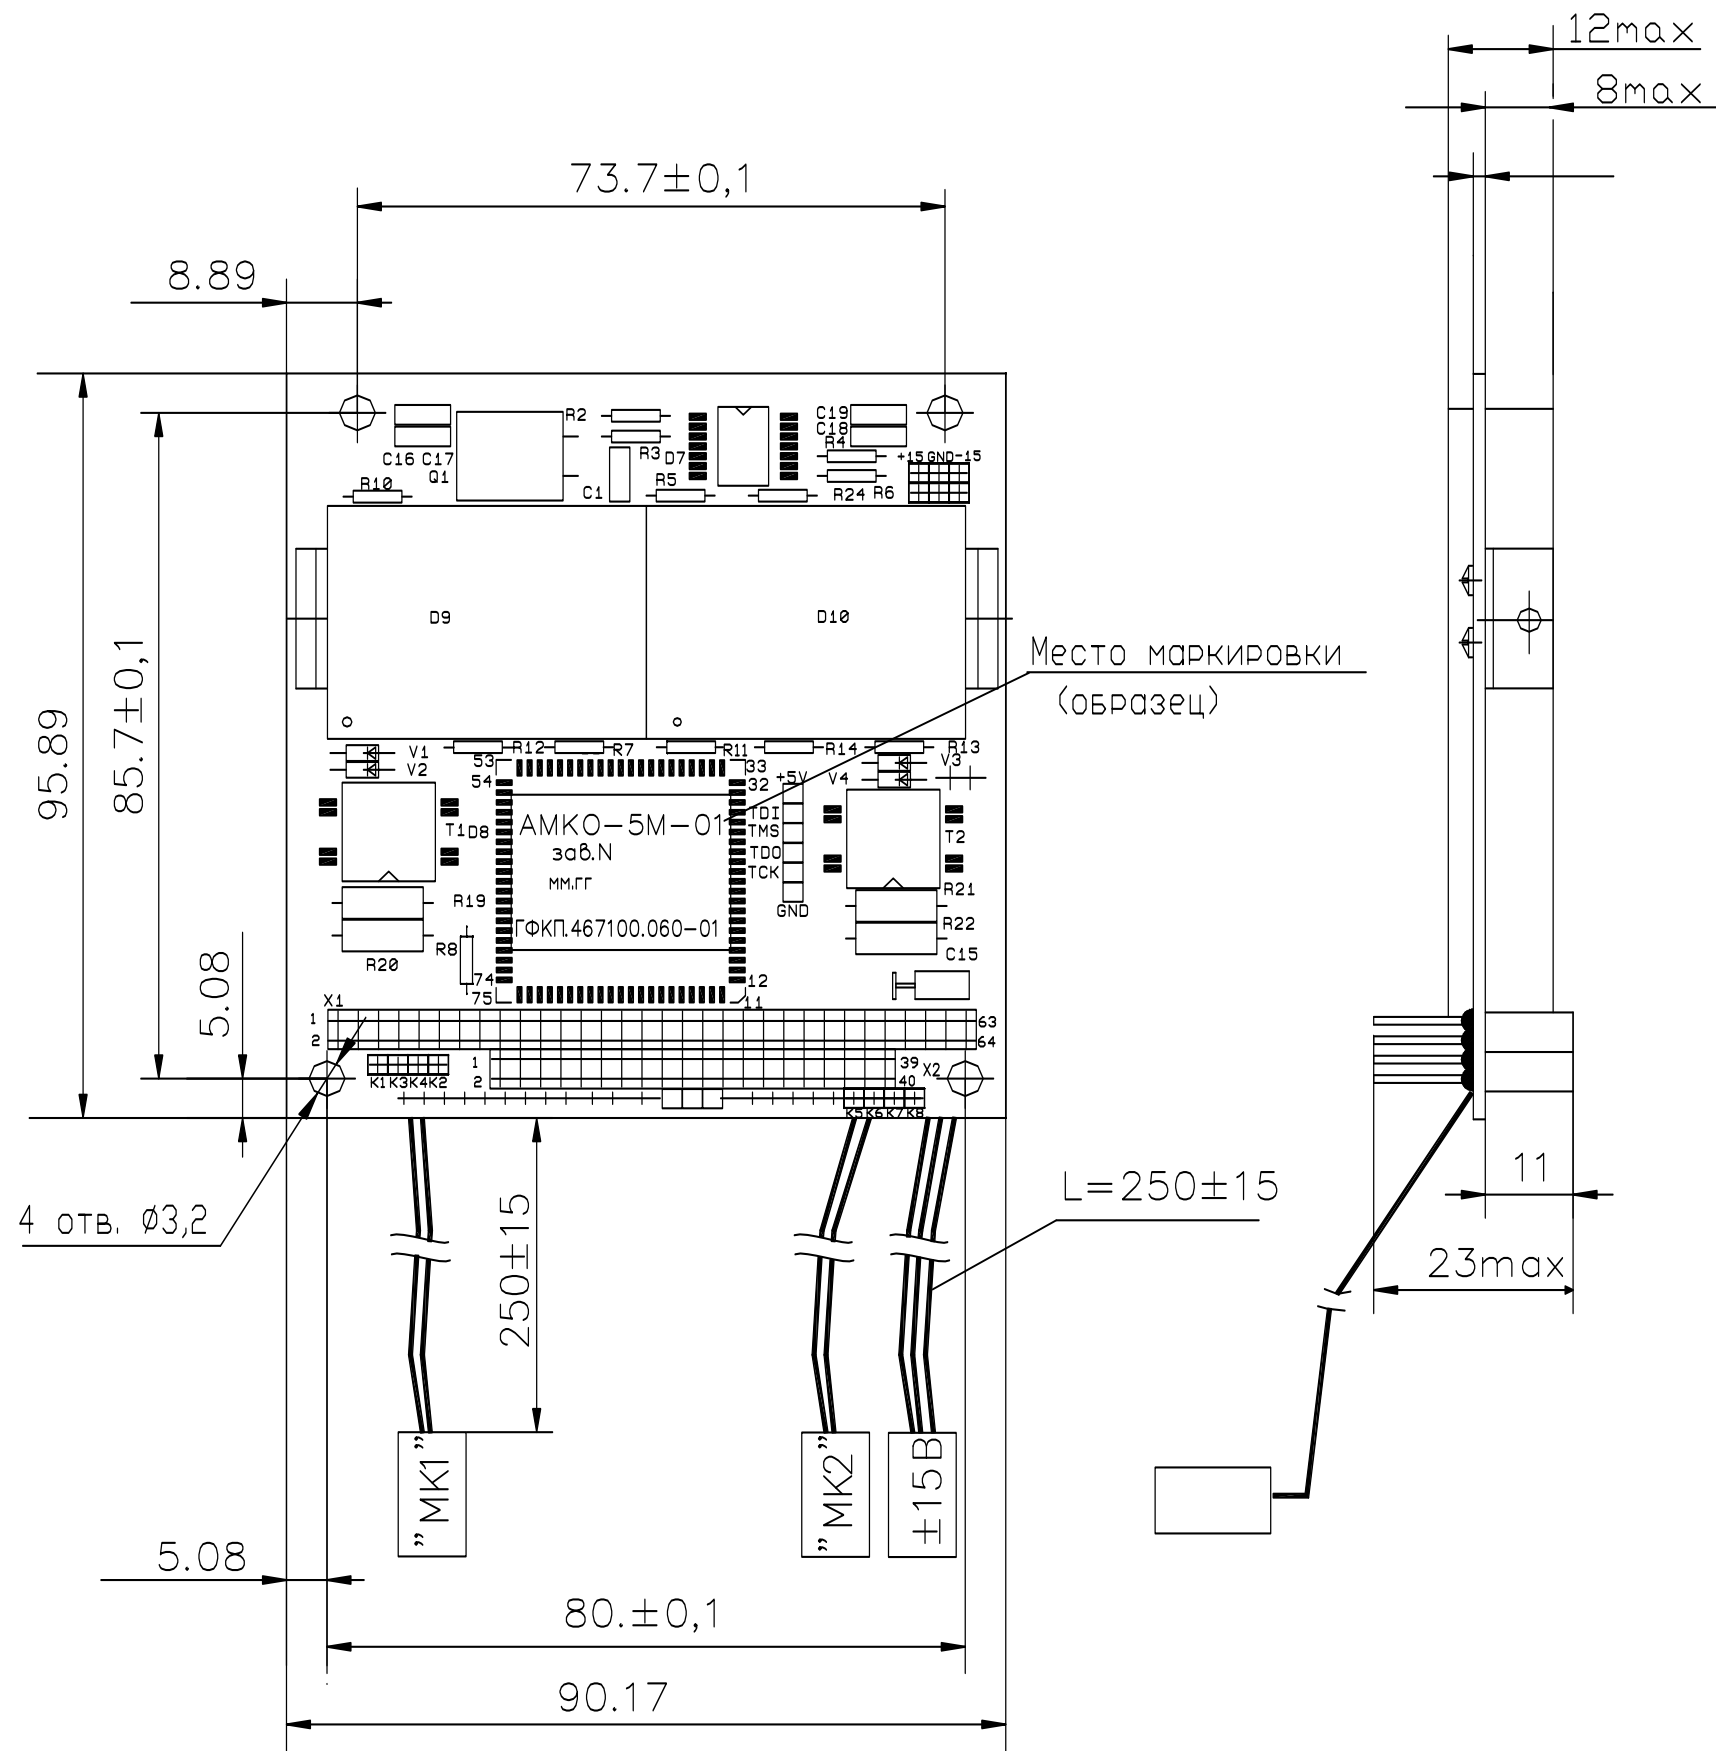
Габаритный чертеж исполнения АМКО-5М-01
